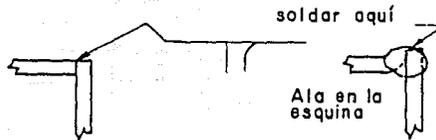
Aplicaciones del símbolo de soldadura en el borde del ala
